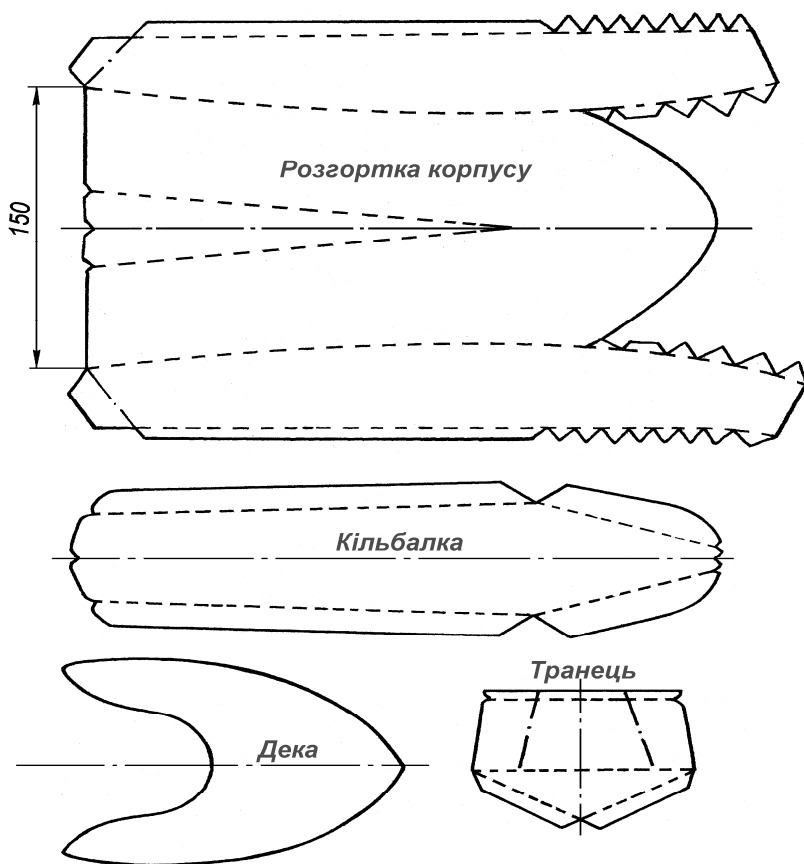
Зменшені креслення розкрою деталей корпусу моделі катера з щільного картону
